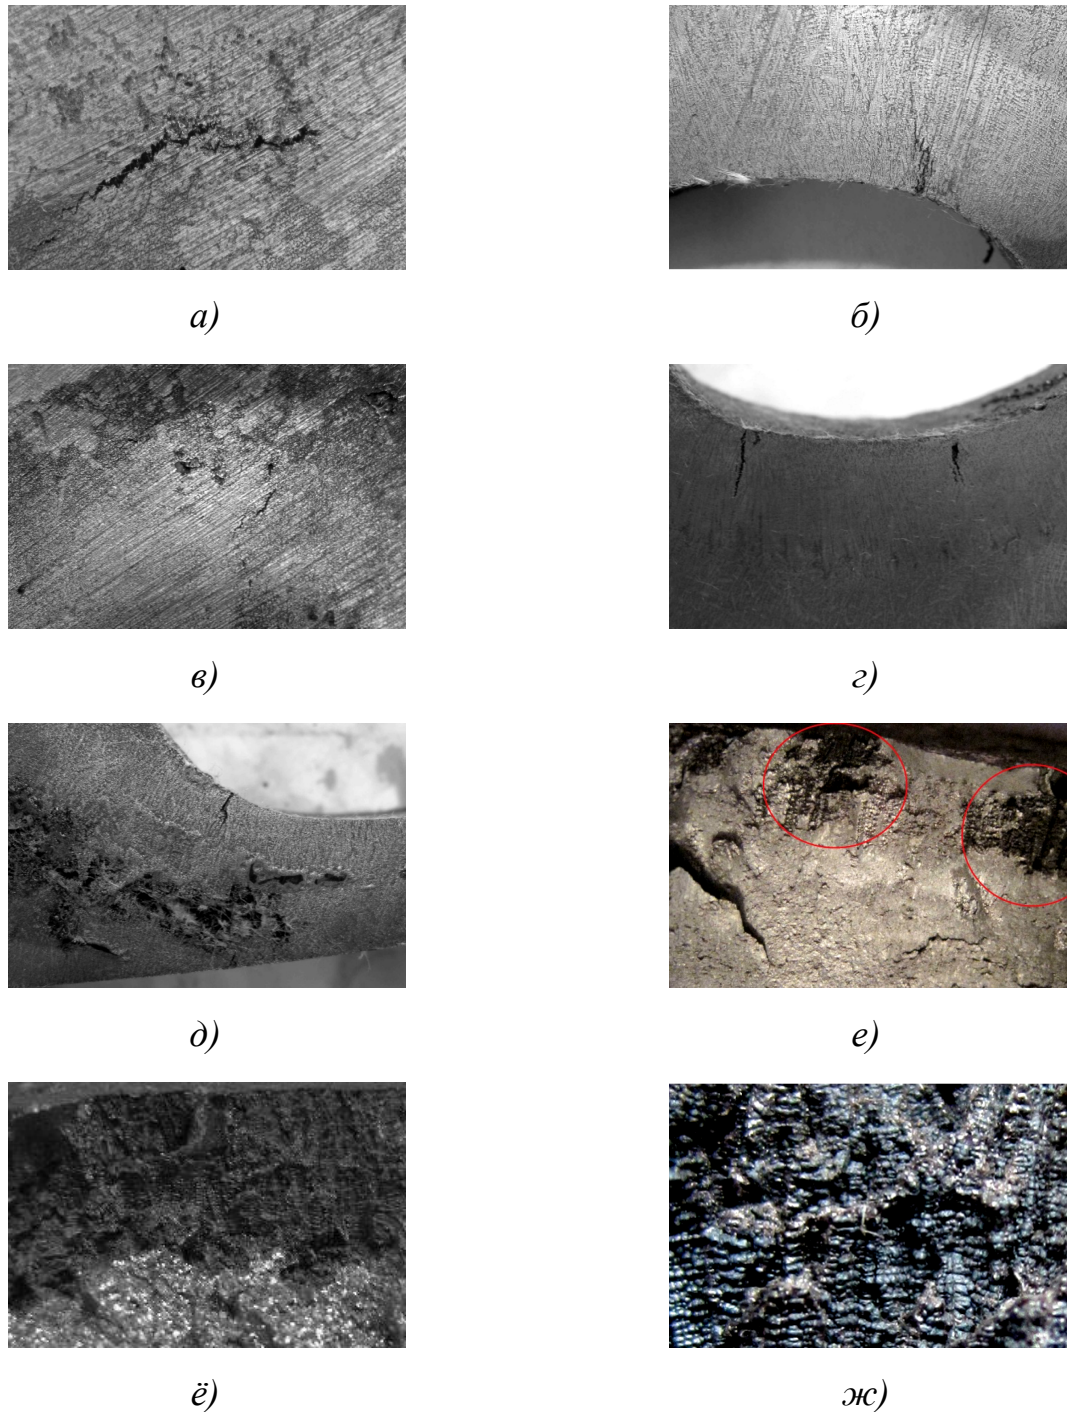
Дефект ГТ в виде надрыва стенки отливки, выявленный в радиусах R55 буксового проема отливки «Рама боковая»: а – наружная поверхность отливки с ГТ (травлено), $\times 2$; б – поперечный разрез стенки (глубина 4 мм), $\times 2$; в – наружная поверхность с ГТ (травлено) $\times 2$; г – поперечный разрез стенки (слева (глубина 7 мм) – явная ГТ, справа (глубина 5 мм) – «скрытая» (подповерхностная) ГТ), $\times 2$; д – поперечный разрез стенки (ГТ (глубина 6 мм) в сочетании с газо-усадочной рыхлотой), $\times 2$; е – излом стенки (выделено красным: слева – явная ГТ, справа – «скрытая» ГТ), $\times 2$; ё – излом стенки, $\times 5$; ж – боковая поверхность ГТ в изломе, $\times 2$
